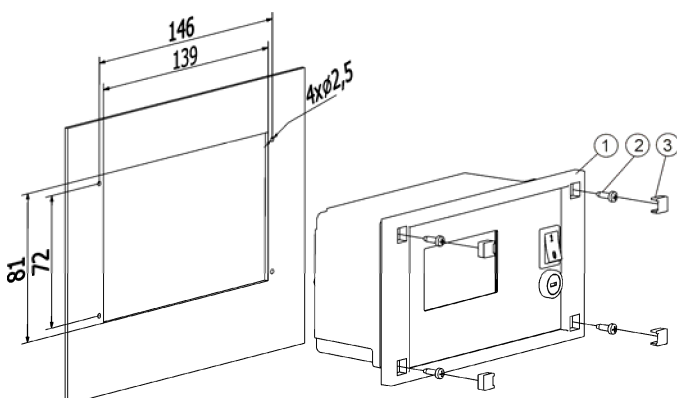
Einbau des Reglers auf der Montageplatte, wo: 1 - Regler, 2 - Blechschraube 2.9x9, 3 - Blende.
